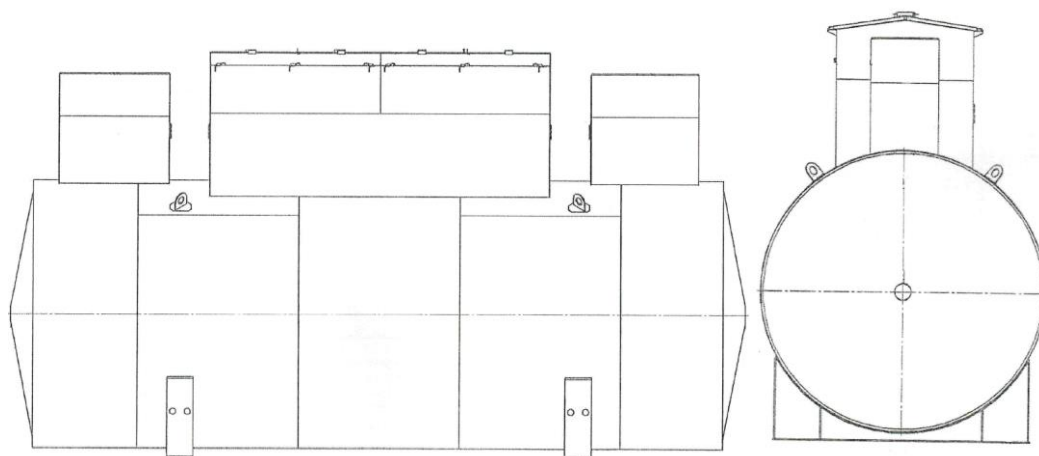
Общий вид резервуаров РГСП-15.2Д
